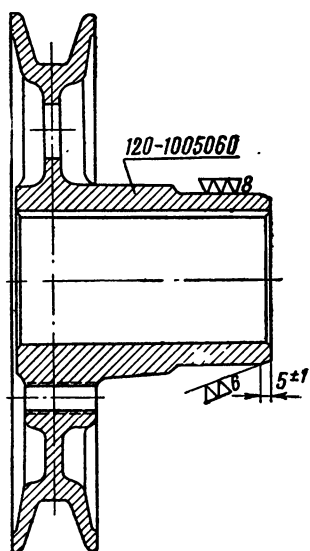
Эскиз изменения шкива коленчатого вала под резиновый сальник
